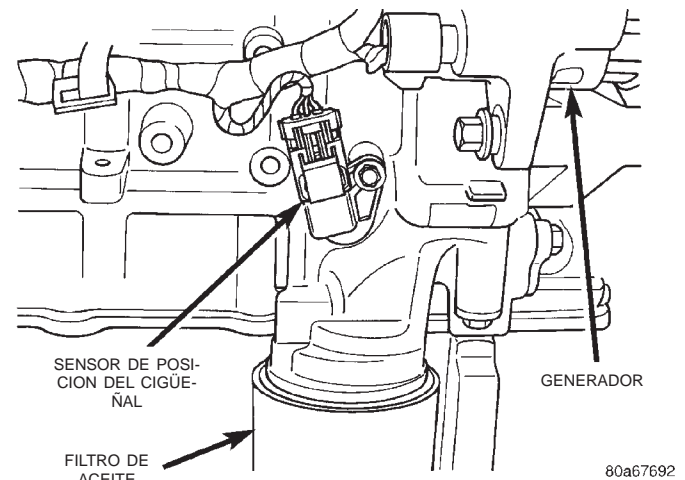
Sensor de posición del cigüeñal—motores de 2.0/2.4L
